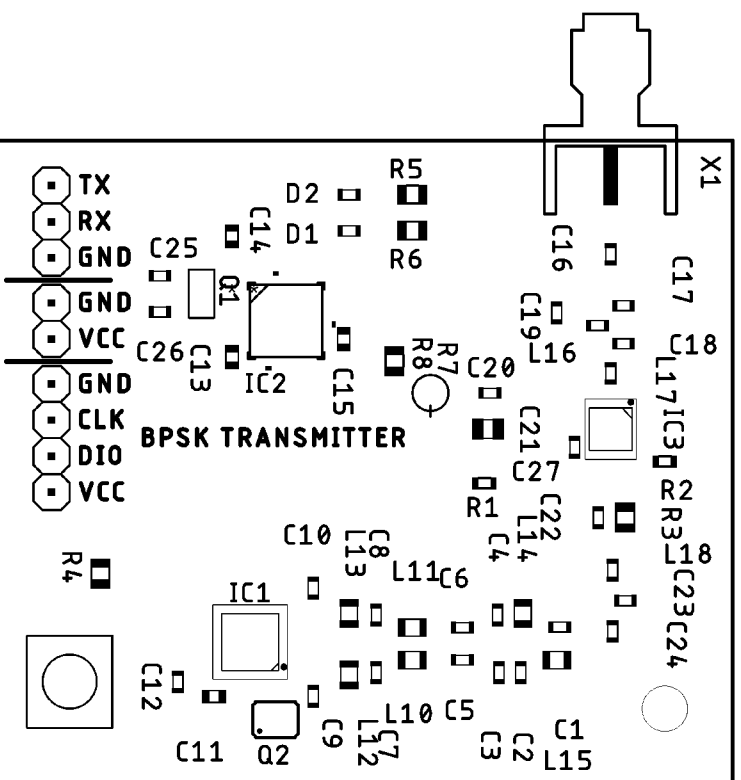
Zobrazení spodní strany desky pomocí programu Fusion 360
